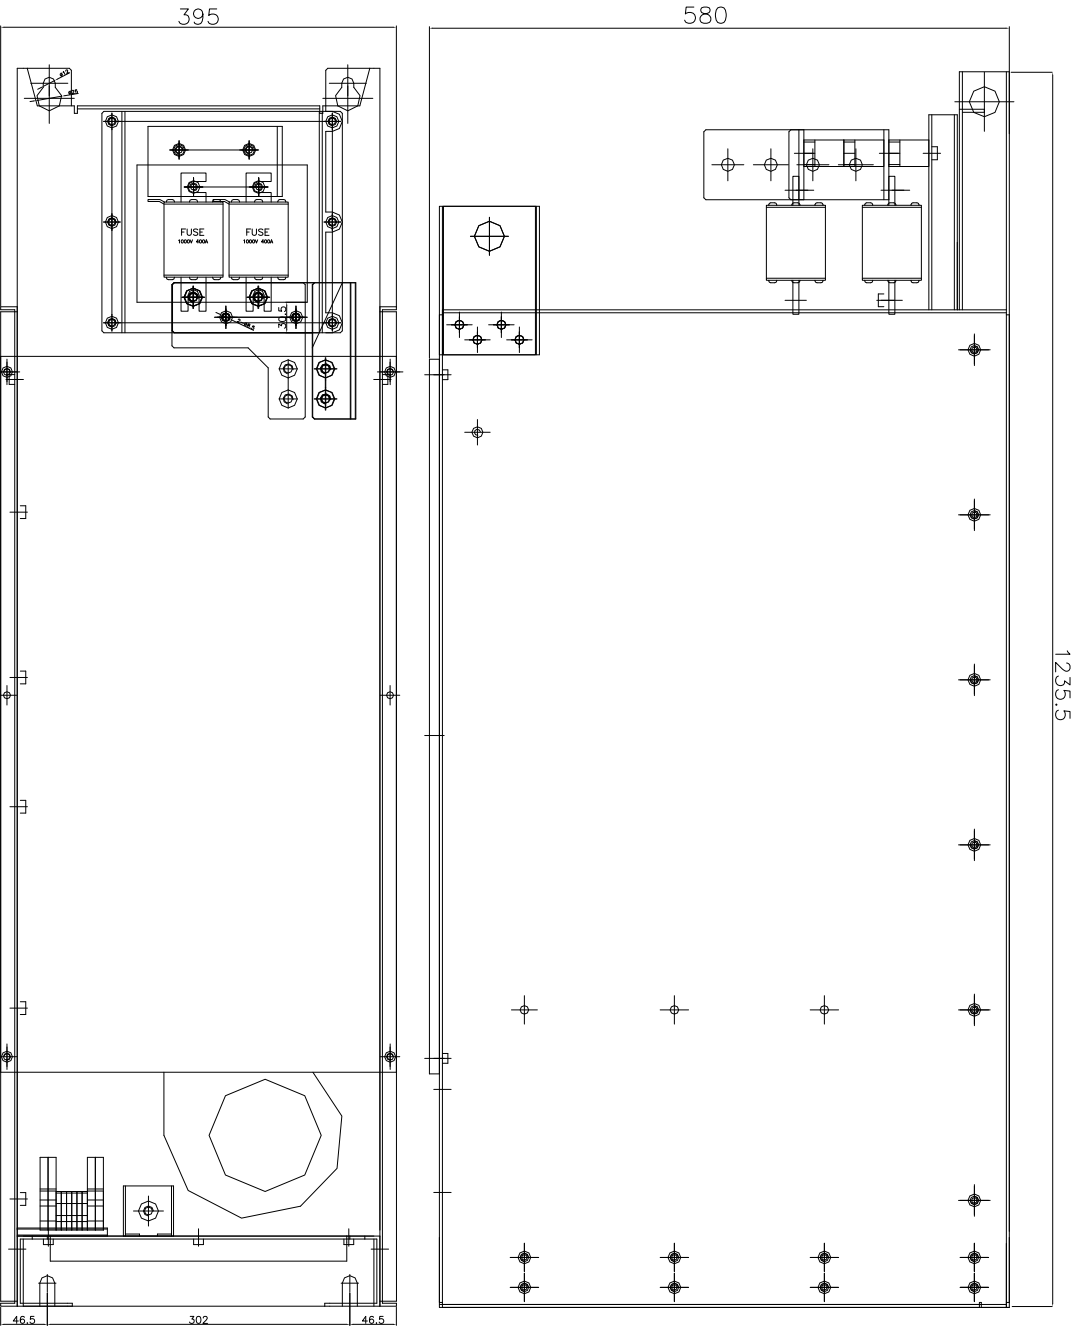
(3) 500VD4N 用 K10B RECTIFIER UNIT 外壳外形尺寸
